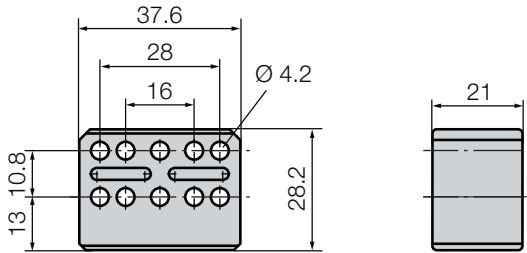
Einbaumaße Positionsgeber BTL6-A-3800-2
